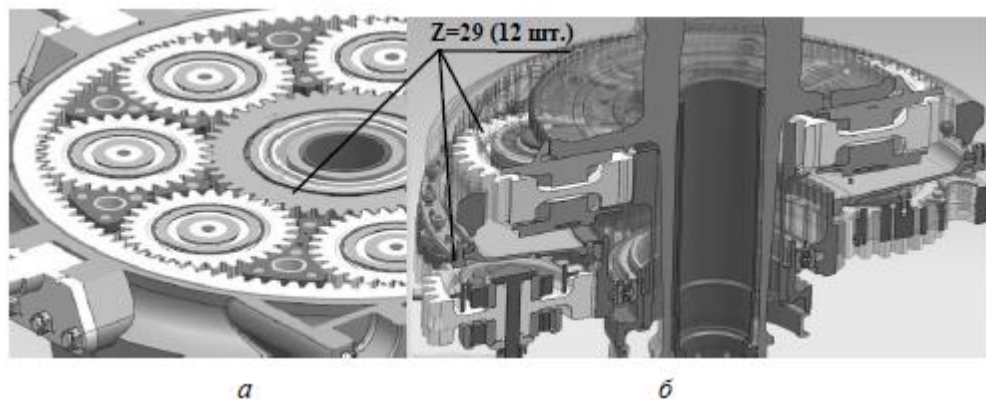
Модель редуктора: а – поздовжній розріз, б – осьовий розріз
